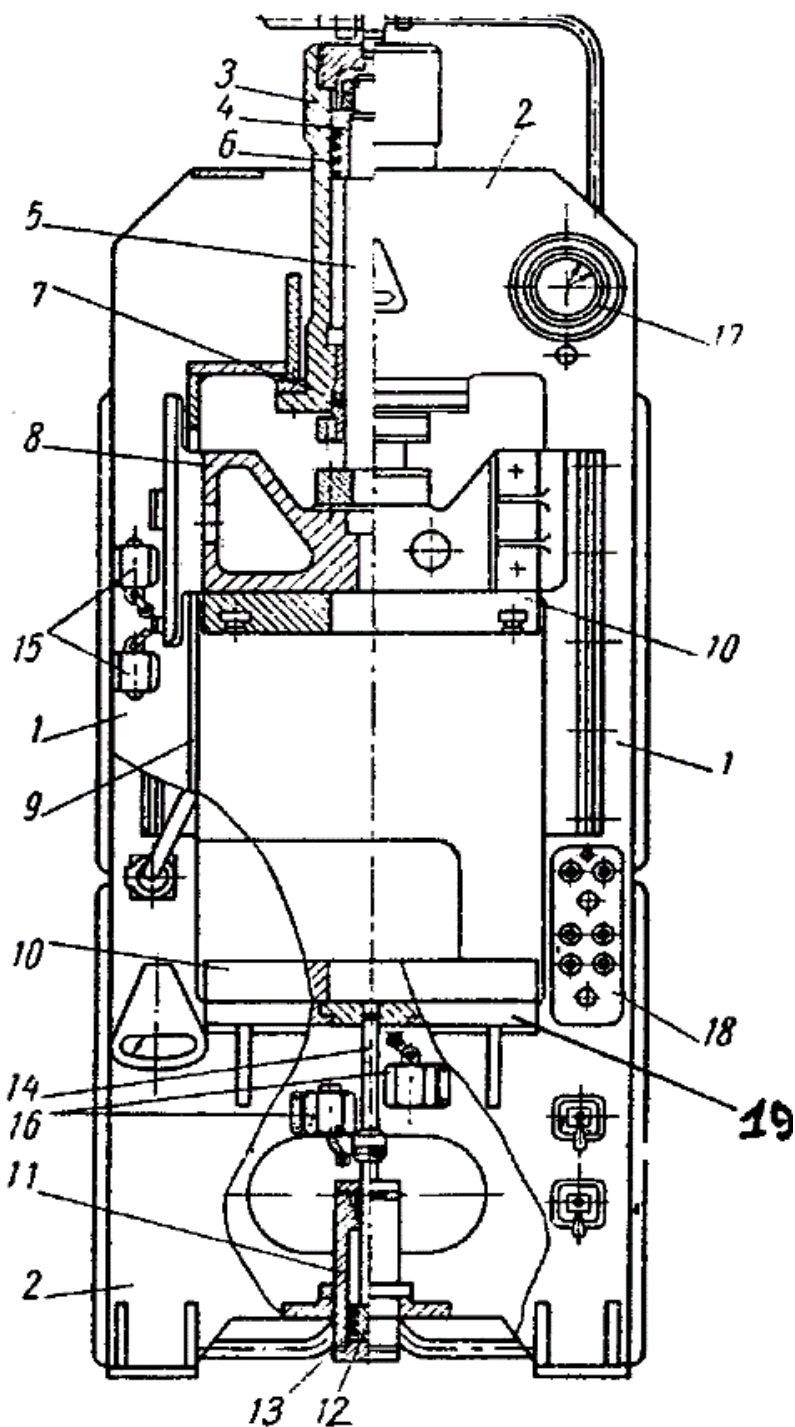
Рамный гидравлический пресс: 1 – стойки; 2 – плиты; 3 – главный гидроцилиндр; 4 – дифференциальный плунжер; 5 – шток; 6, 7 – уплотнительные манжеты; 8 – подвижная верхняя плита; 9 – направляющие; 10 – верхняя и нижняя рабочие плиты; 11 – гидроцилиндр выталкивателя; 12 – дифференциальный плунжер выталкивателя; 13 – уплотнительные манжеты; 14 – шток выталкивателя; 15 – конечные выключатели (ограничители хода) верхней плиты; 16 – конечные выключатели хода выталкивателя; 17 – электроконтактный манометр давления; 18 – пульт управления пресса; 19 – стол
